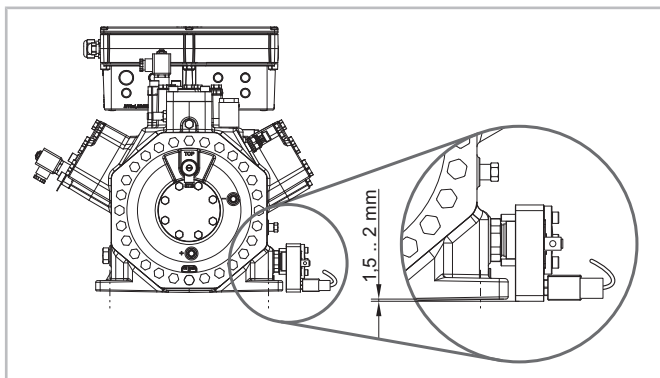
OLM-IQ peut dépasser vers le bas par chaque millimètres.
